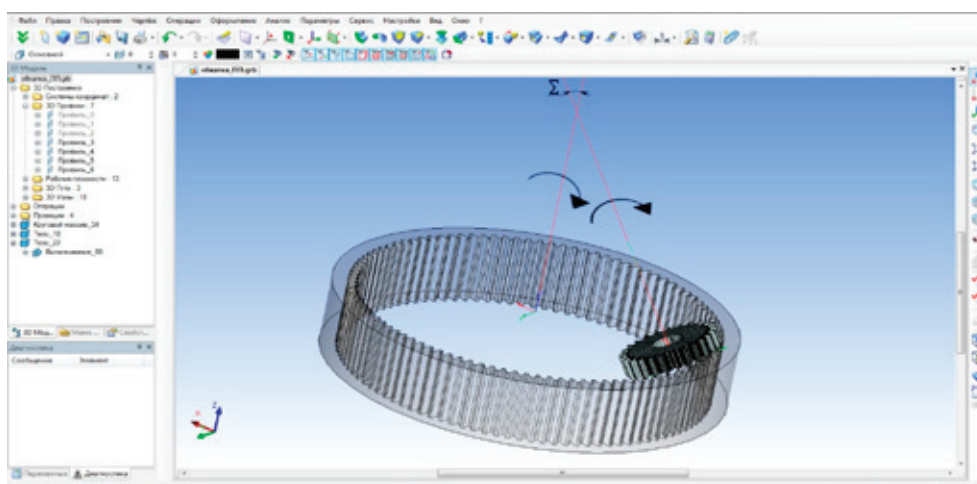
Схема внутреннего станочного зацепления обкаточного резца и обрабатываемого зубчатого колеса с внутренними зубьями
